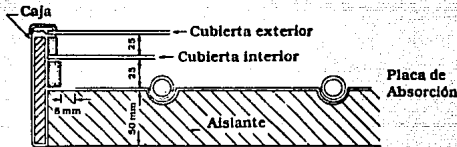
CORTE TRANSVERSAL DE UN COLECTOR PLANO CON DOS CUBIERTAS DE VIDRIO.
